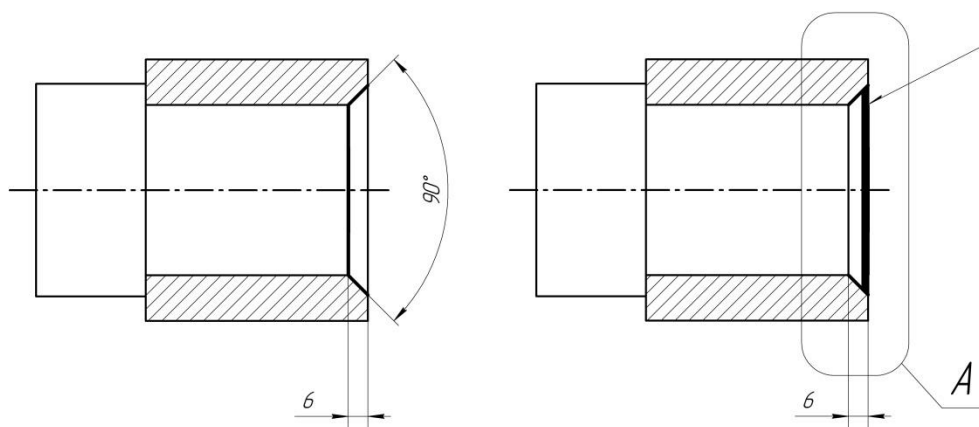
Ремонтный чертеж детали поверхности, которой подлежат ремонту сваркой, пайкой, нанесением металлопокрытий
